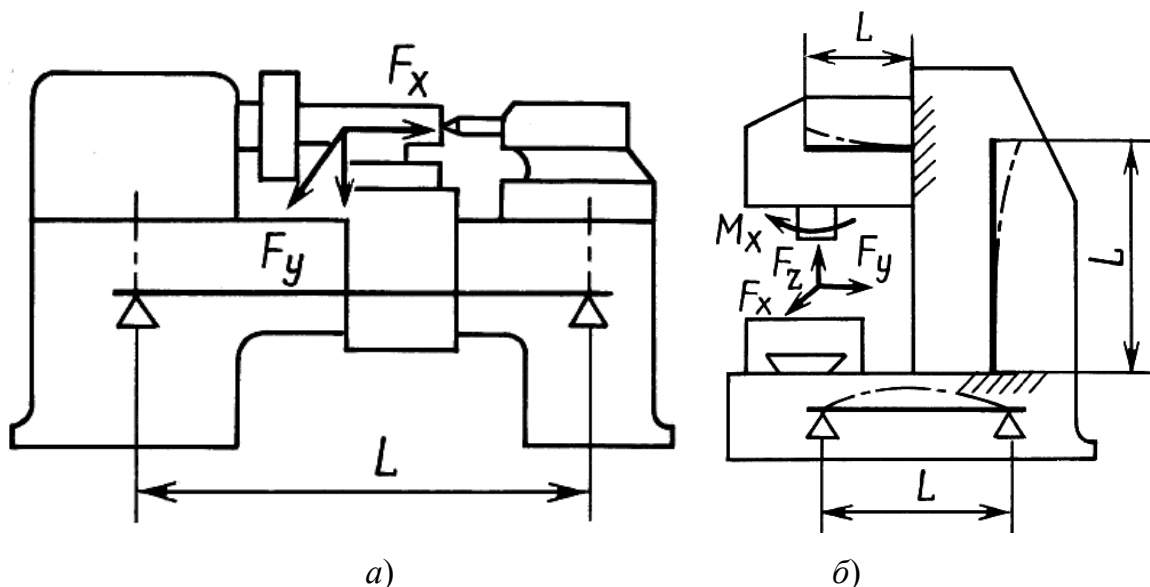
Расчетные схемы для базовых деталей станков:
